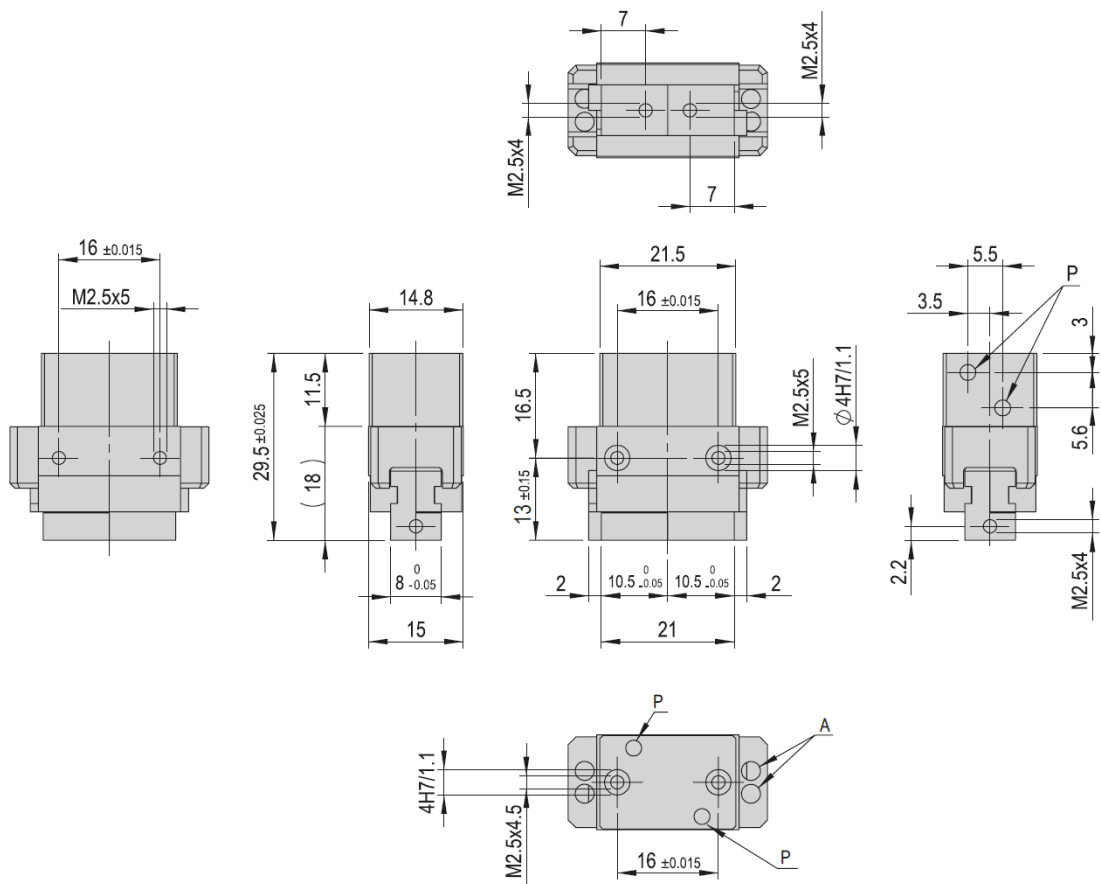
Masszeichnung Präzisionsgreifer PG 12
